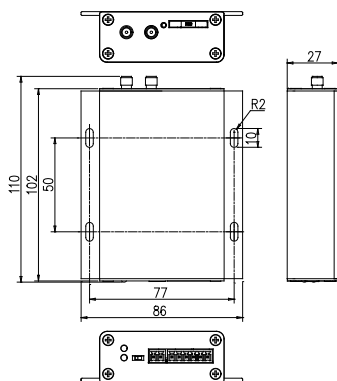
Габаритные размеры для модели IP20 (настенный корпус)
